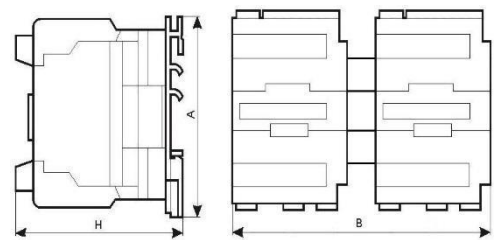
Контактор реверсивный ПМЛ-5560М
